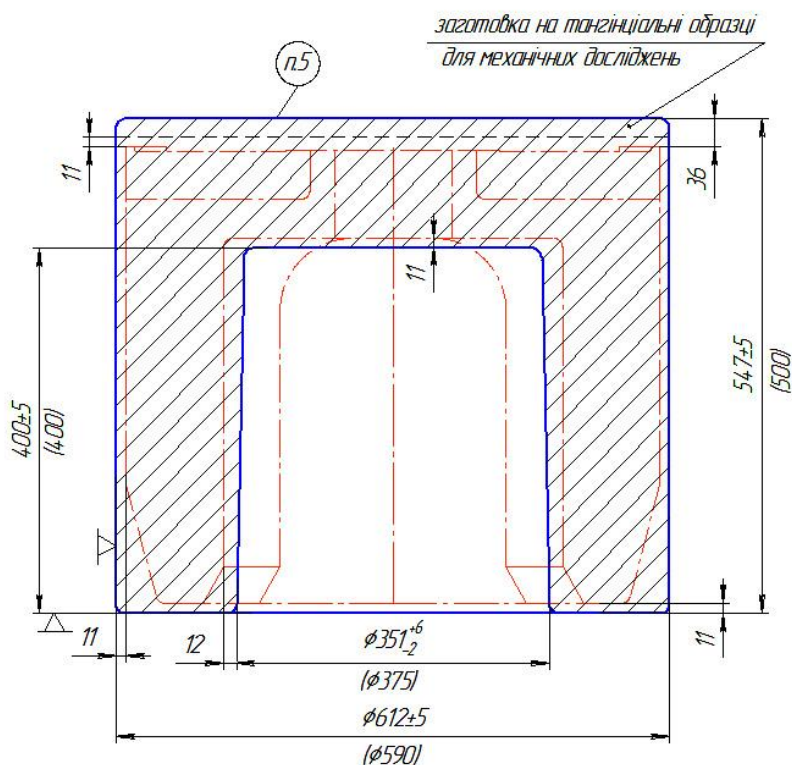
Ескіз заготовки муфти П6-ВА4-А.15.09
